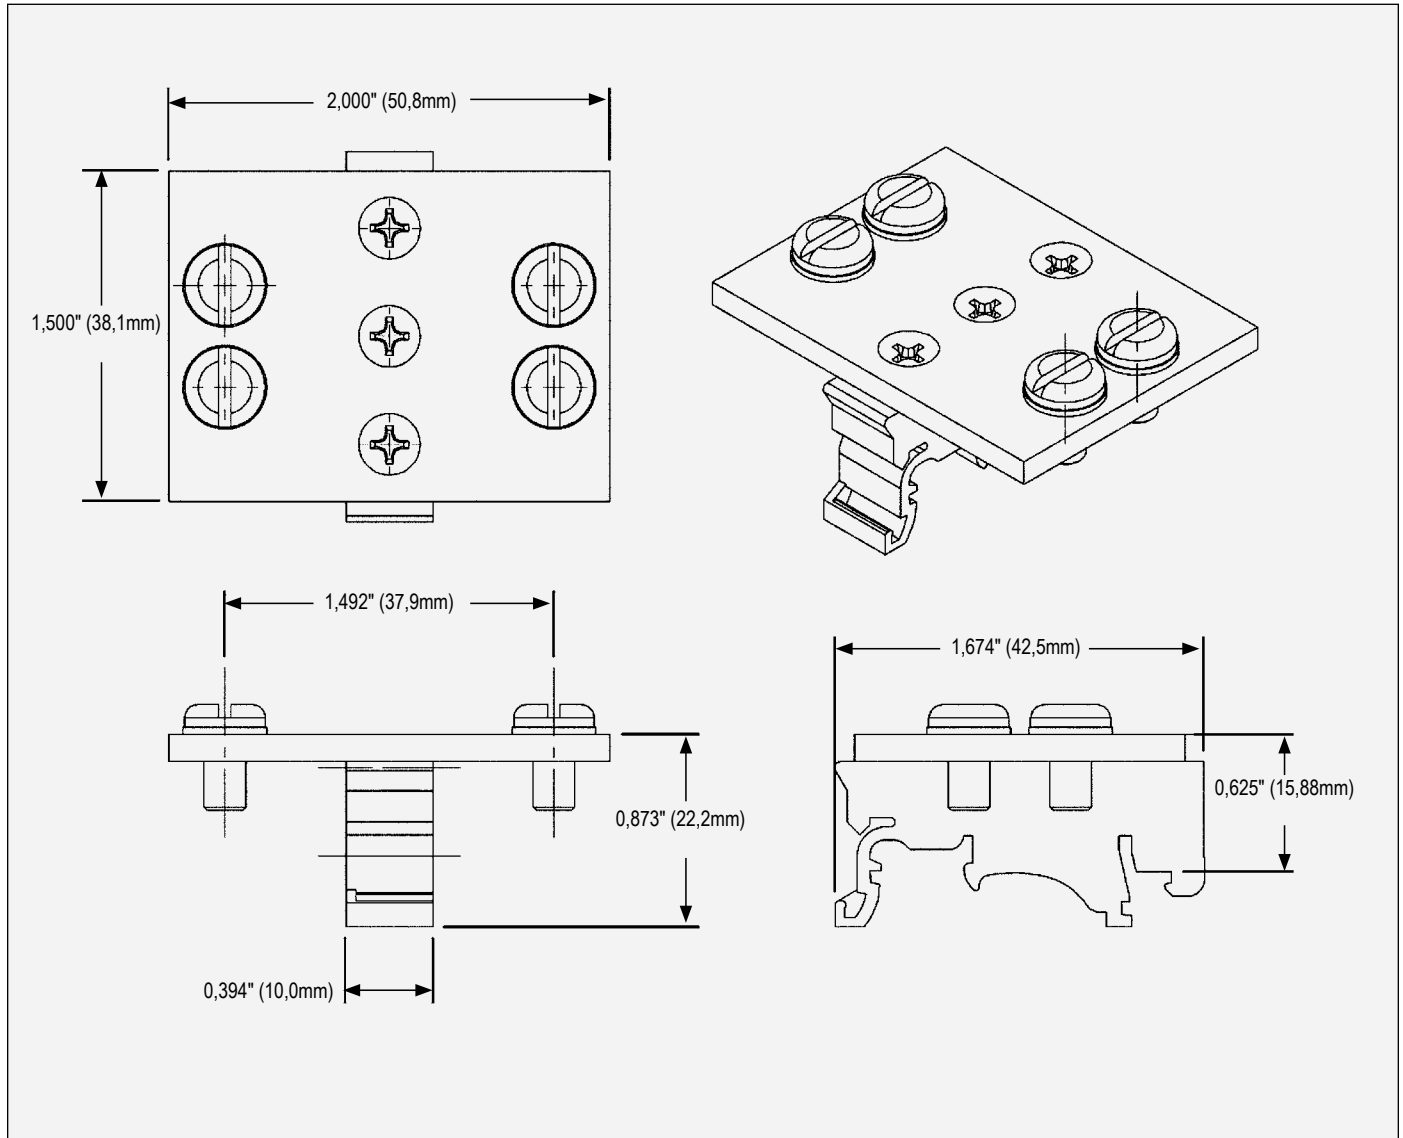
Maße des DIN-Schienenbefestigungskits für Magnete
